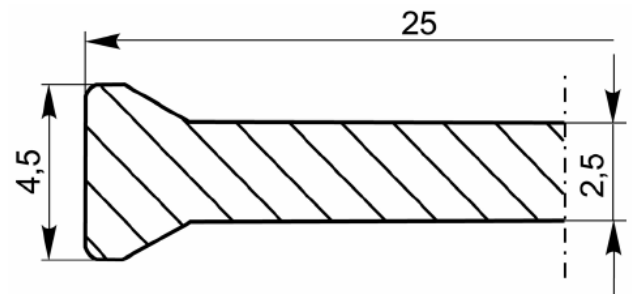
Fensterisolierprofil mit den Hauptabmessungen in mm
